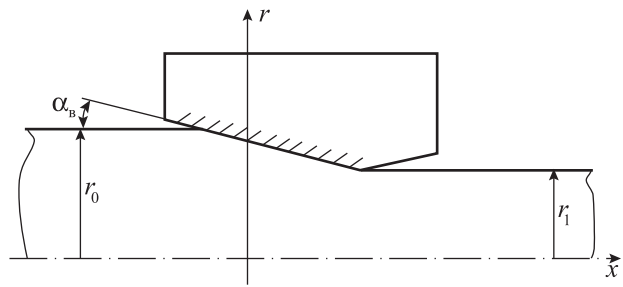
Схема деформирования композитной заготовки в конической матрице
